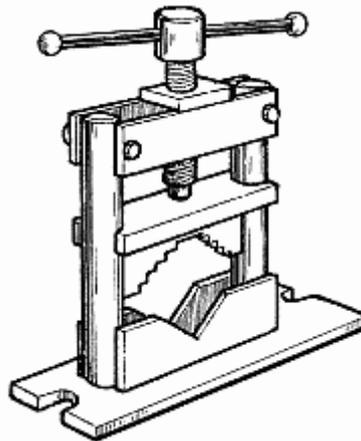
Нарезка резьбы с помощью трубного прижима.
